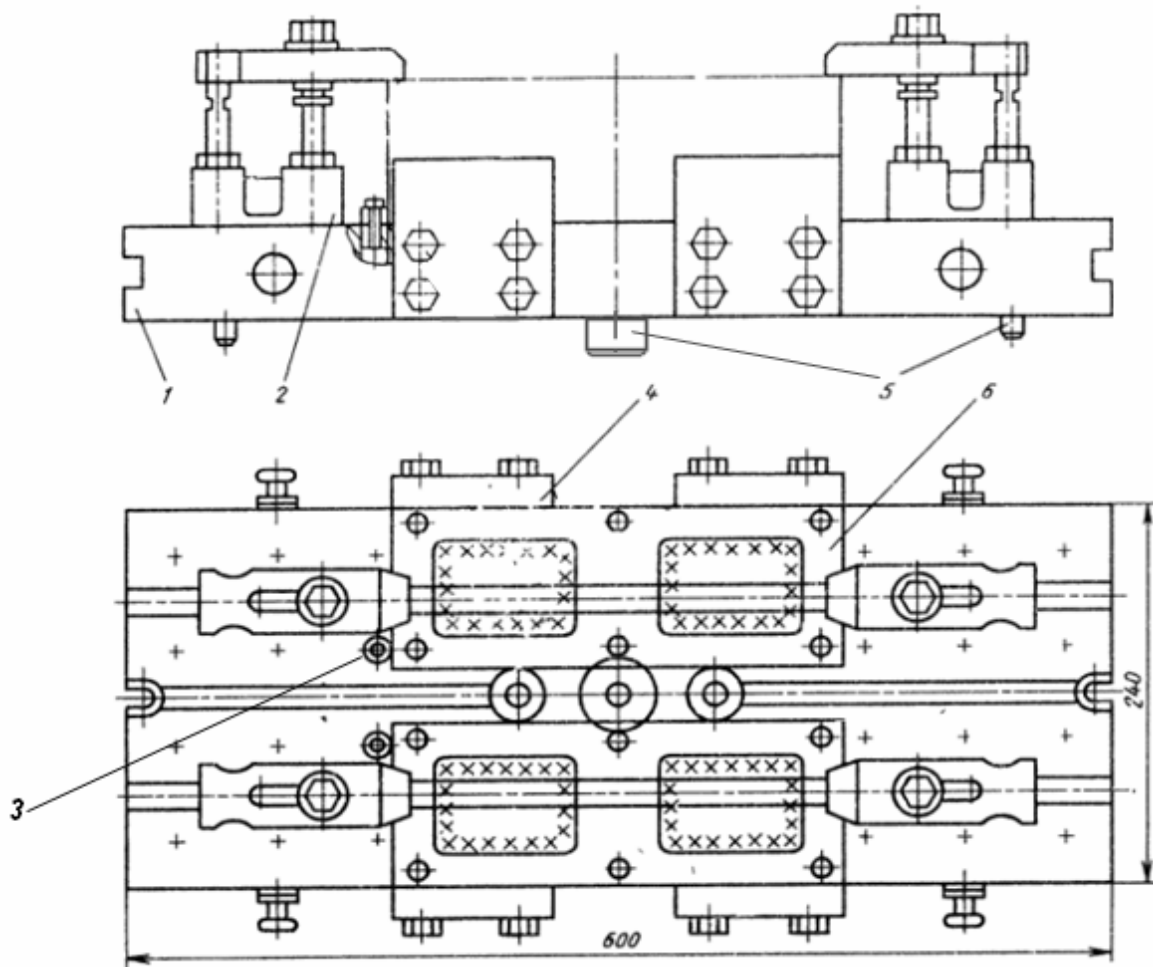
Верстатний пристрій, складений з елементів системи ЗРП для встановлення заготовок деталей типу «Корпус»
